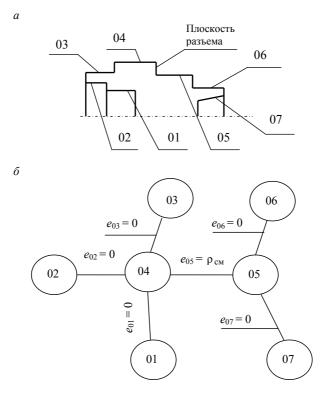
Заготовка и дерево ее эксцентриситетов
